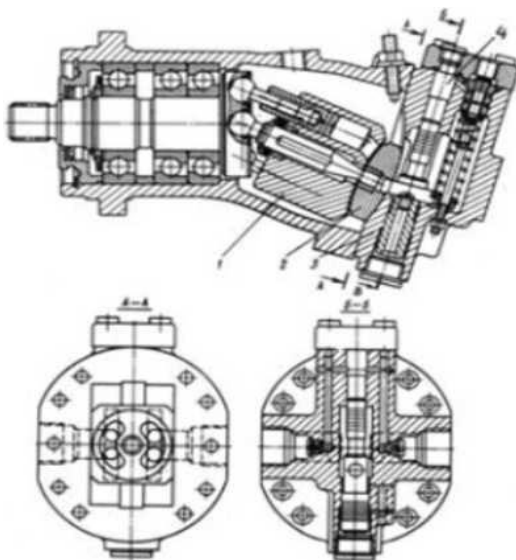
Конструкция поворотного устройства блока цилиндров регулируемого насоса типа 313
